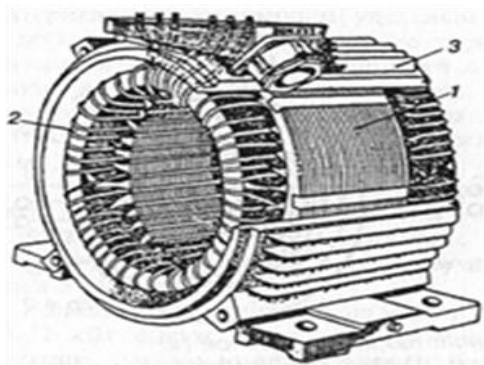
Статор машины переменного тока: 1 — сердечник; 2 — обмотка; 3 — корпус
